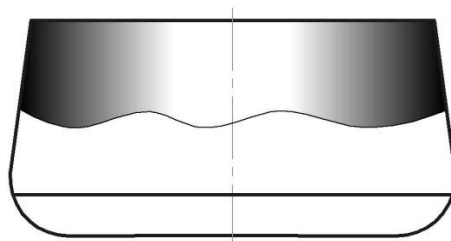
Форма поверхности среза вырубленной детали при нормальном зазоре.
